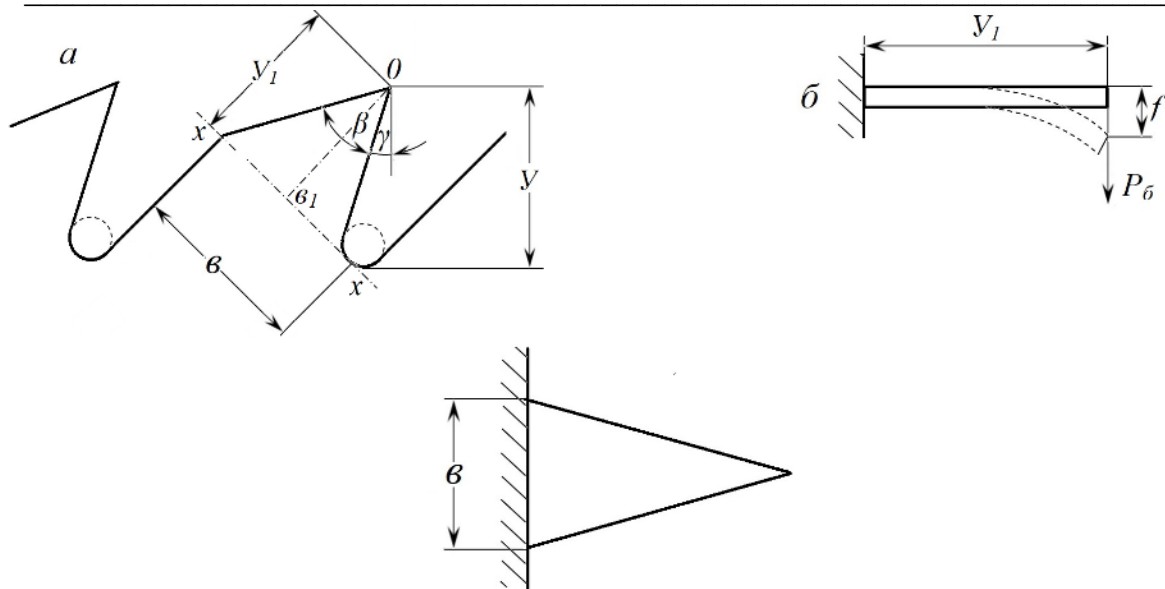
Схема розрахунку зуба пили на поперечний вигин: а – параметри зуба пили; б – жорстке закріплення зуба пили у вигляді трикутної балки
